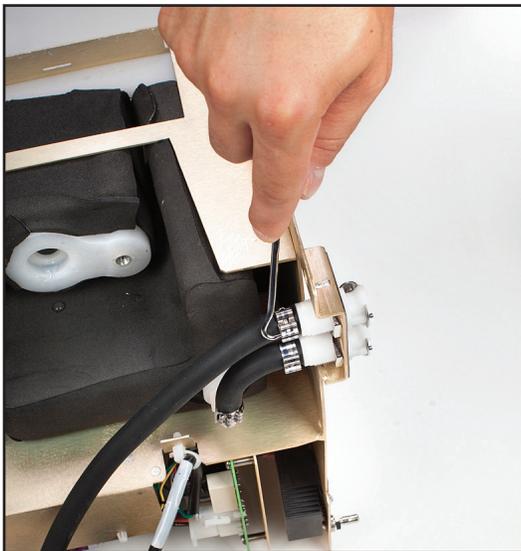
Abra la abrazadera que conecta el tubo de la bomba de refrigeración con la válvula de drenaje
